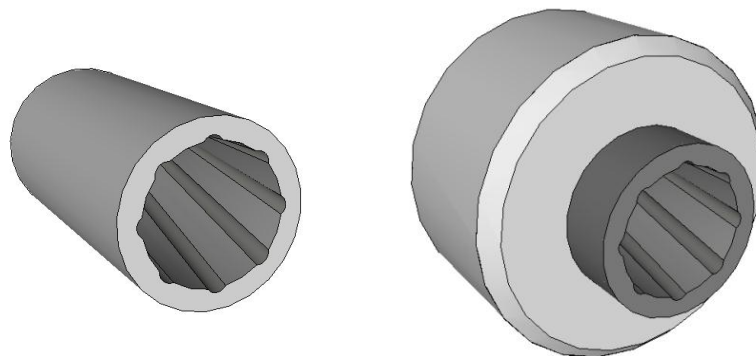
Representação do Tubo Suporte e com o Anel montado.
